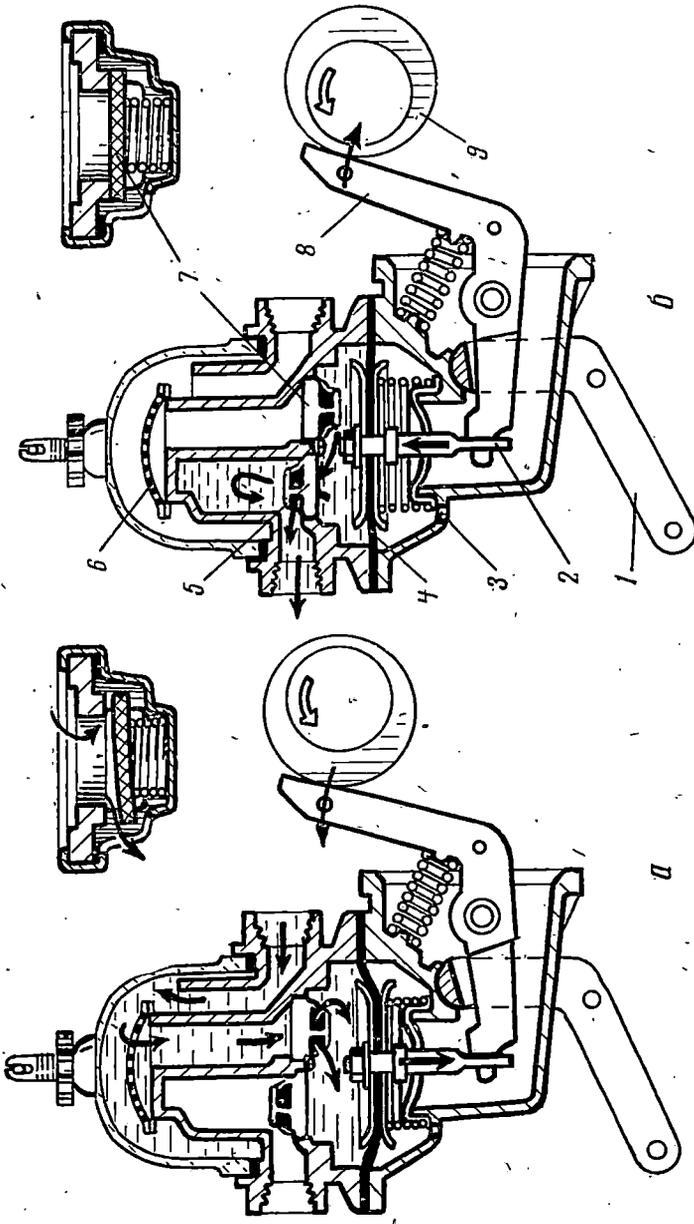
Топливный насос автомобиля ГАЗ-51А:
